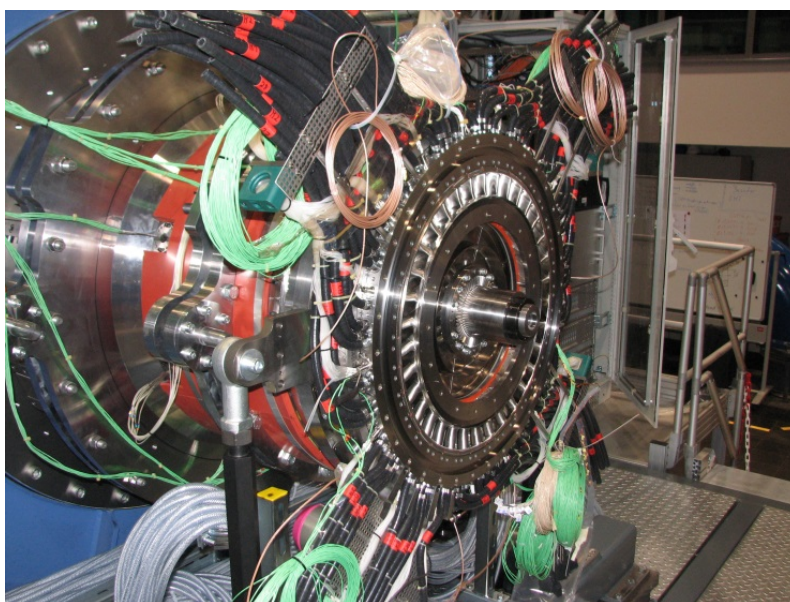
Rotor 2 Gehäuse und Stator 2 Montage
